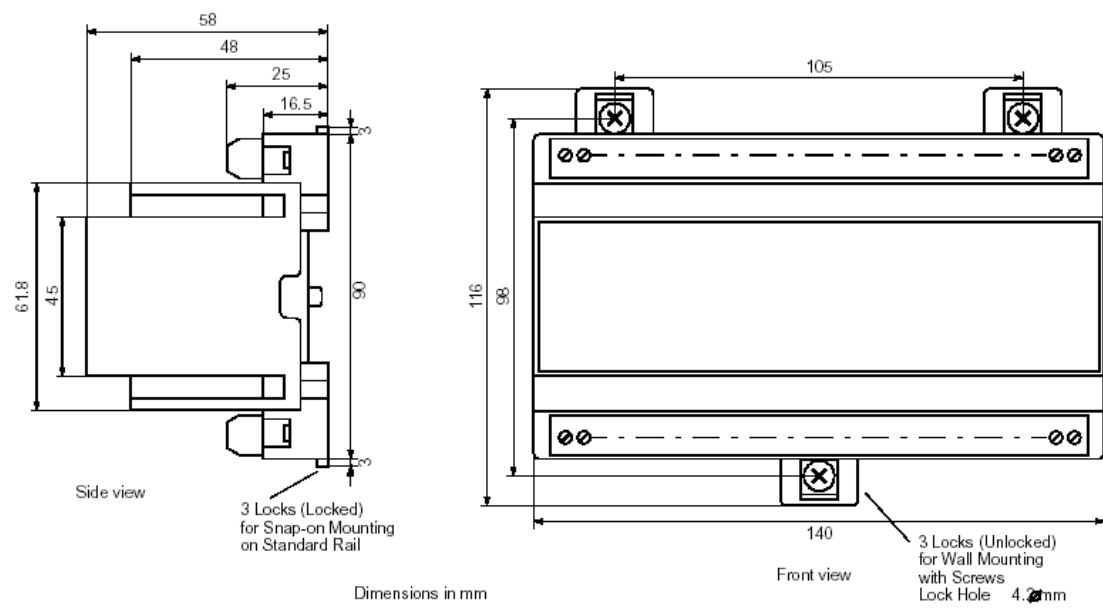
温度转接盒 7XV5662-*AD10-0000 尺寸
